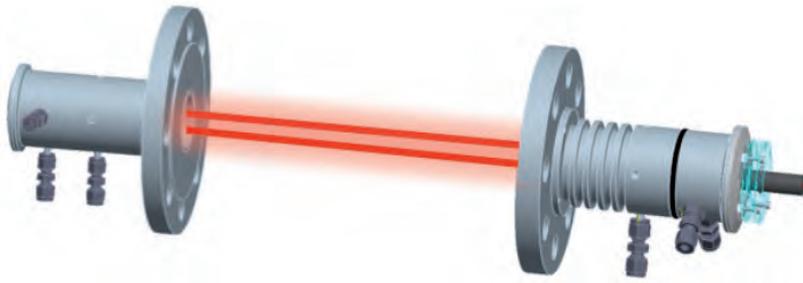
Montaje del conjunto de puntero láser / blanco reflectante en el cabezal TDL.
